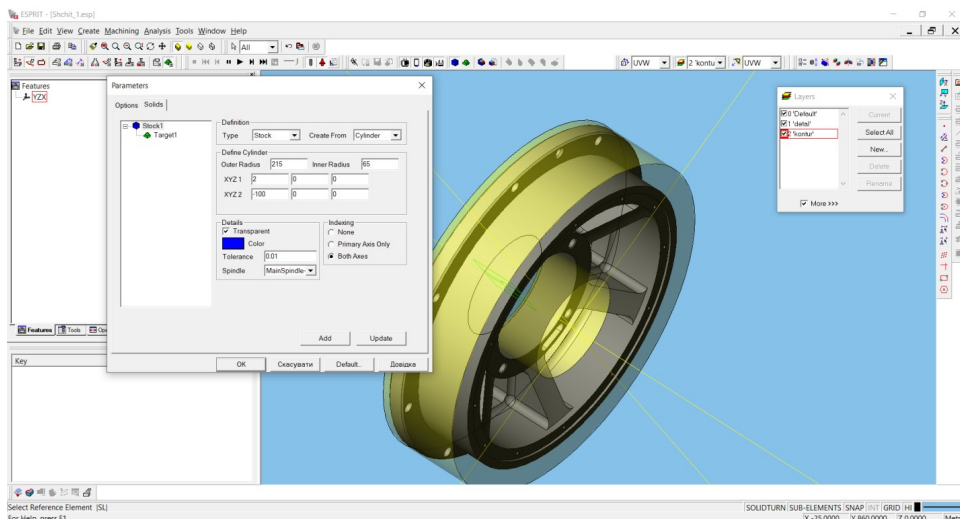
Параметричне моделювання заготовки деталі «Корпус підшипника» для ЧПК-обробки
